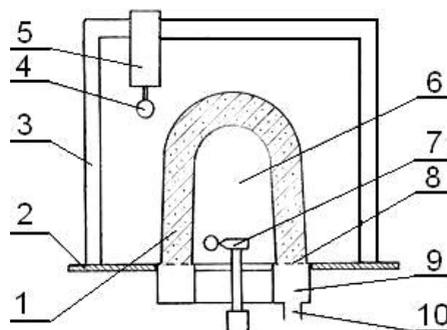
Схема установки для 3D-деформирования: 1 – сыпучий материал; 2 – стол; 3 – П-образный портал; 4 – инструмент с ДЭ; 5 – подвижный привод; 6 – заготовка; 7 – привод с инструментом; 8 – перфорированная стенка; 9 – вакуумпровод; 10 – штуцер
